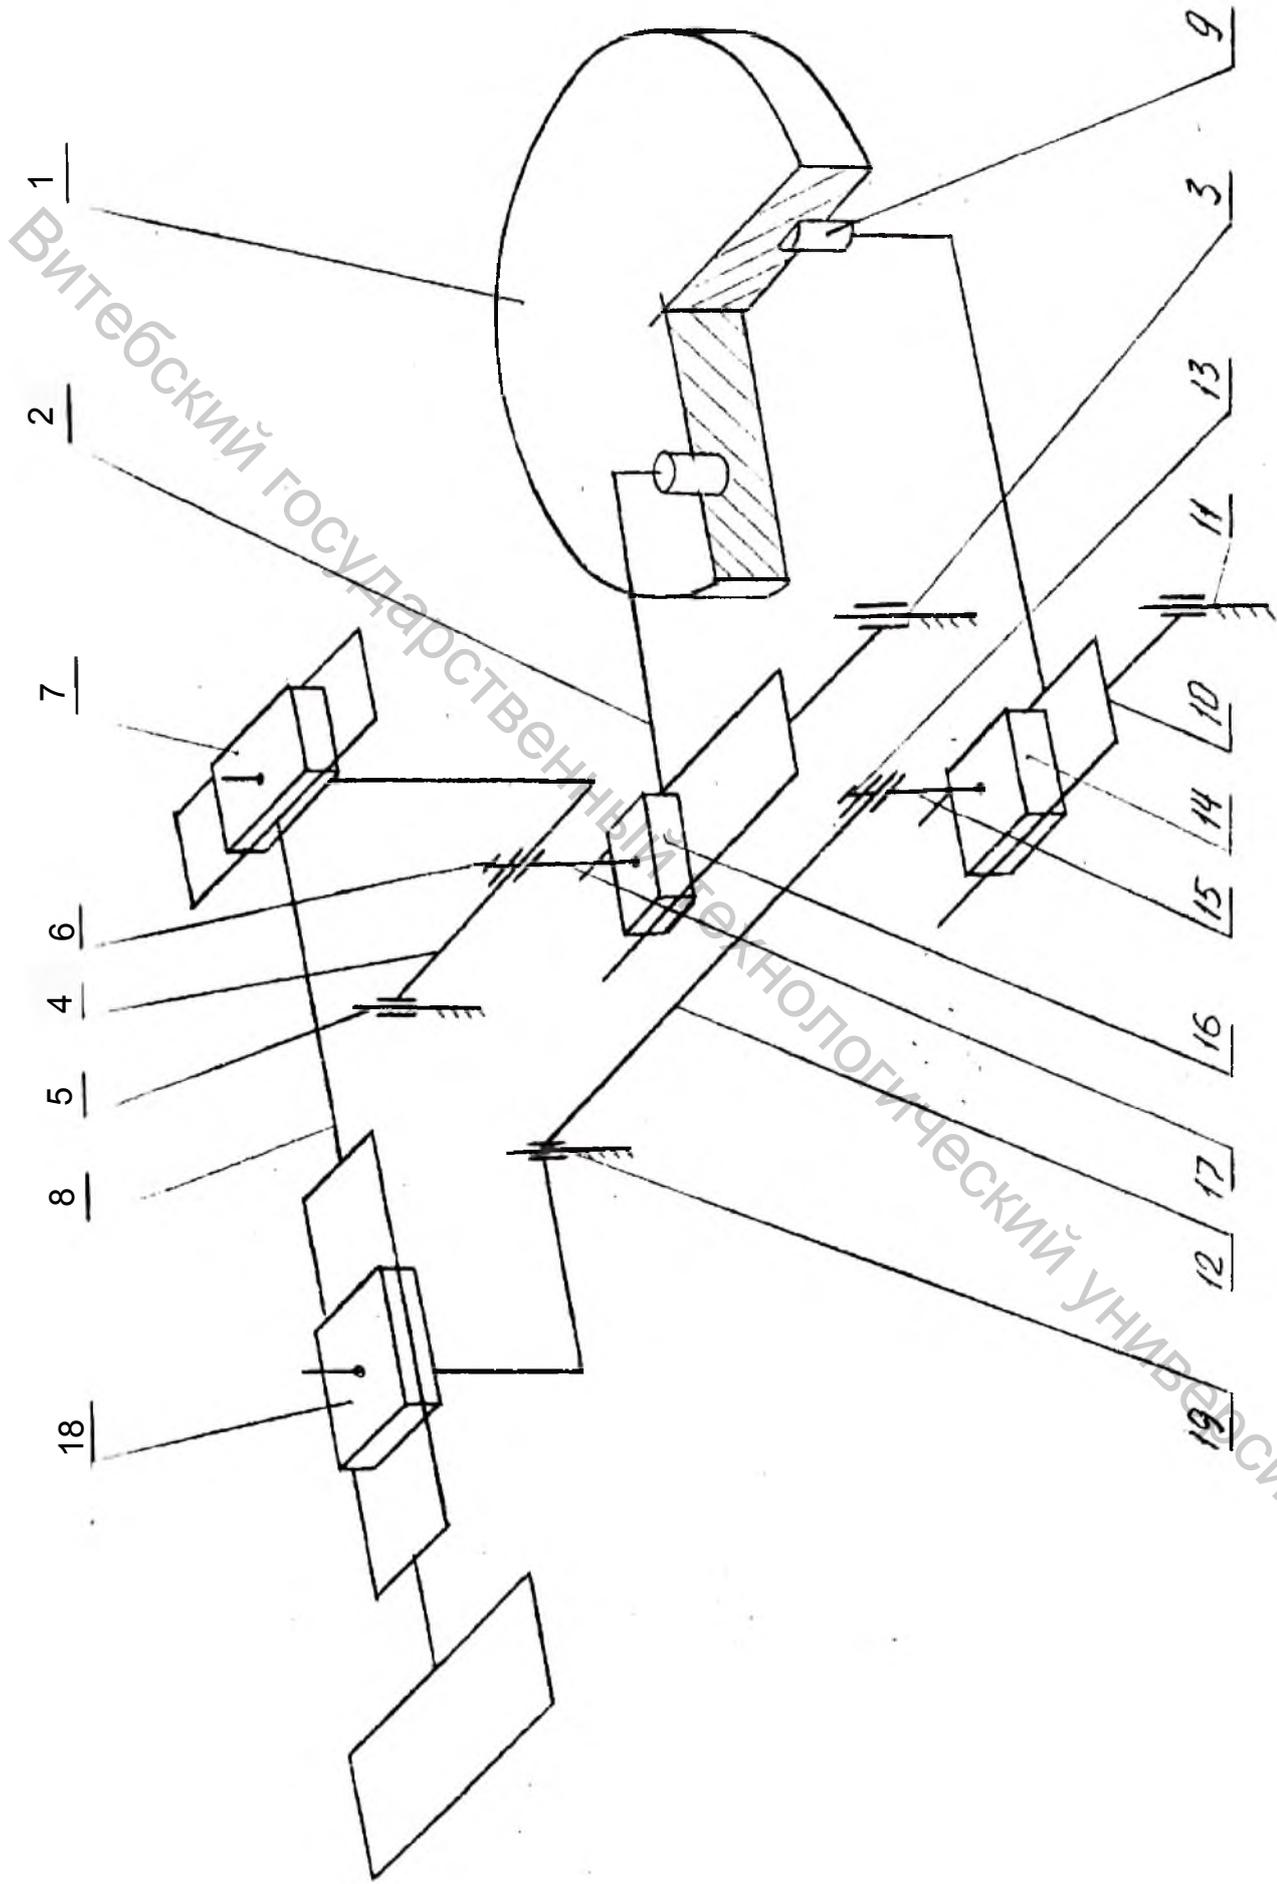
Механизм подачи материала закрепочного полуавтомата К-1850 класса фирмы "Джуки"
